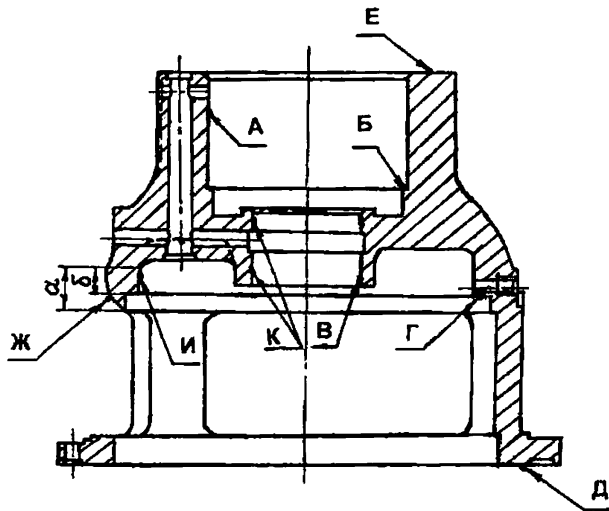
Корпус подшипника (поз. 3, рисунок 56)
